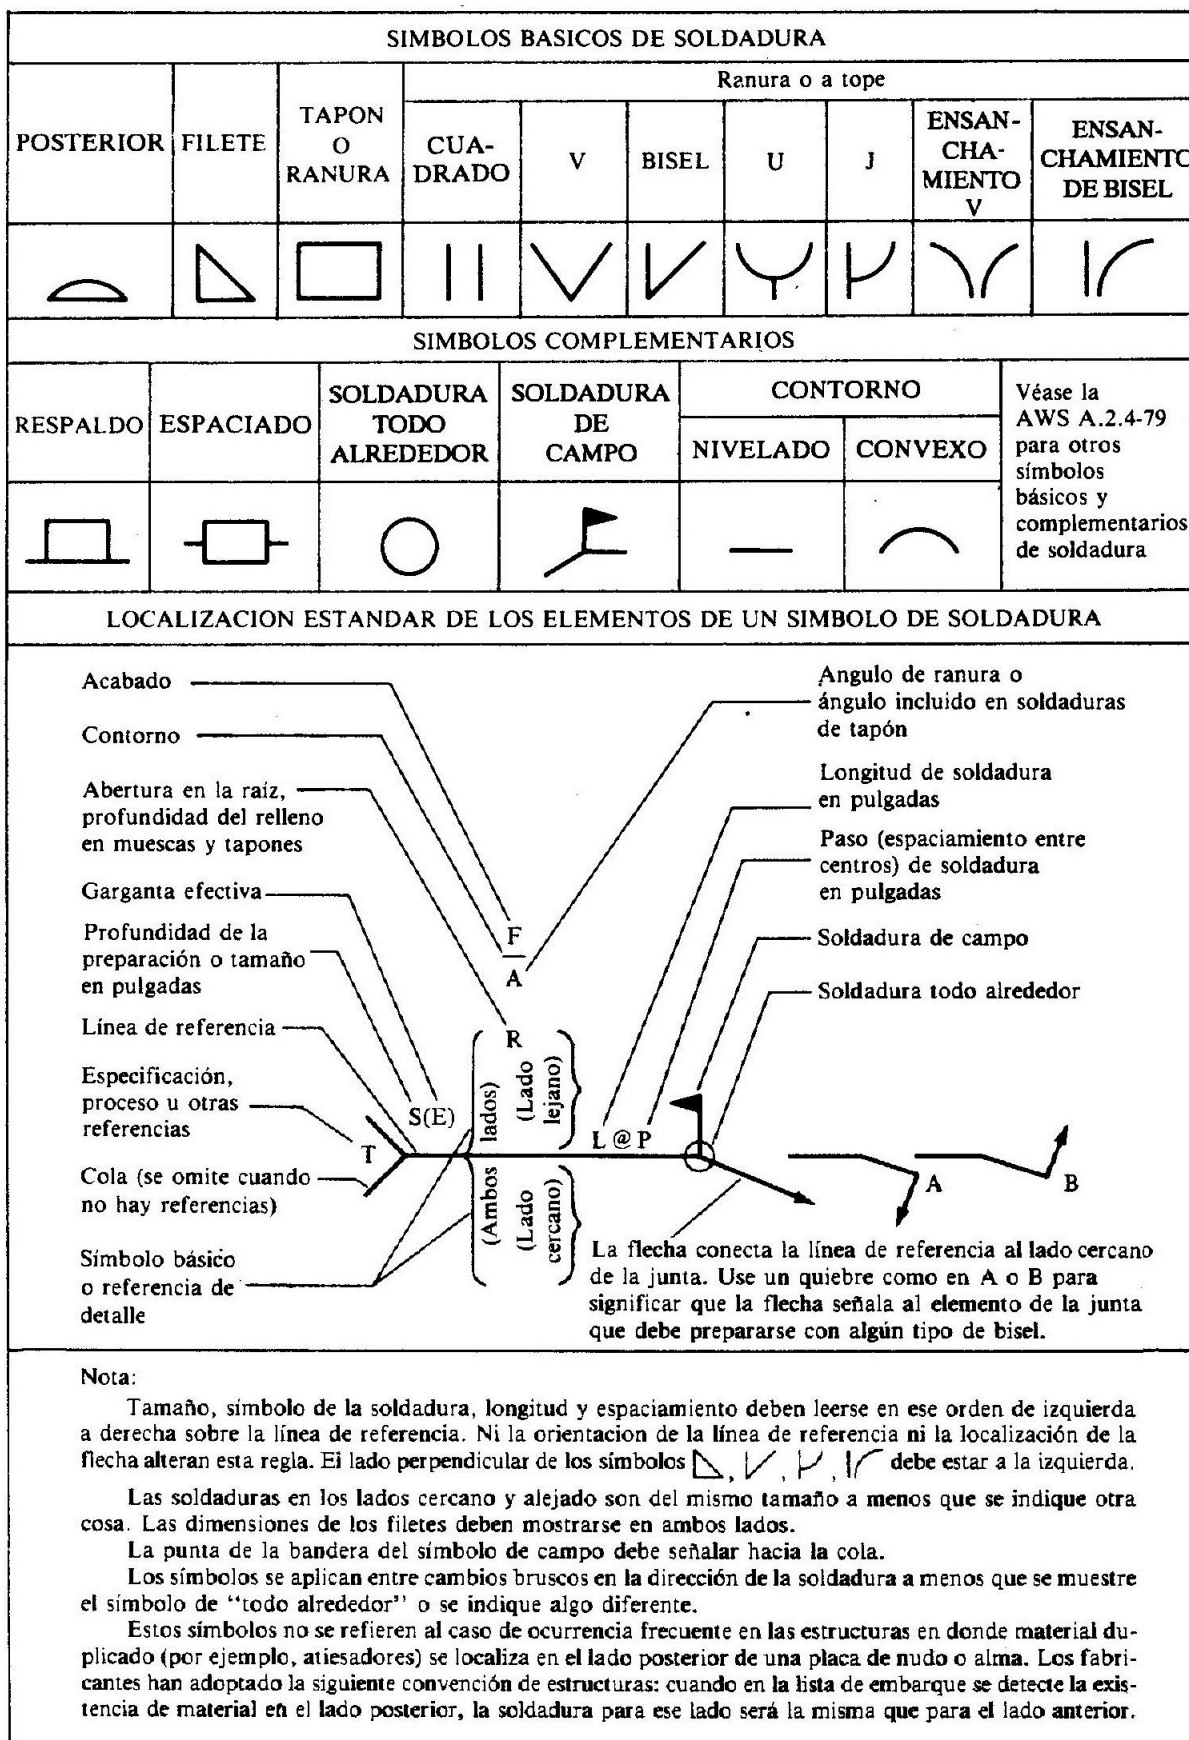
Simbología básica de soldaduras de acuerdo al AWS. (Ref. 16)
